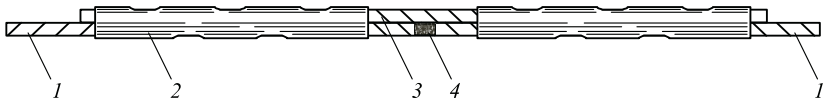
Использование двух соединителей и термитной сварки:
